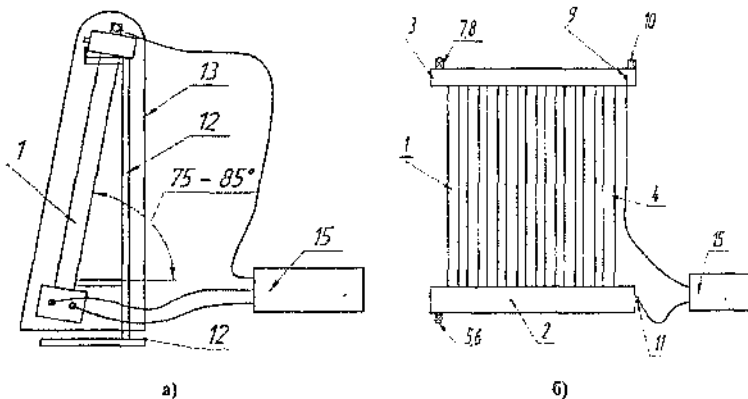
Пароконденсатный нагреватель а) (вид сбоку); радиатор пароконденсатного нагревателя б) (вид спереди)
